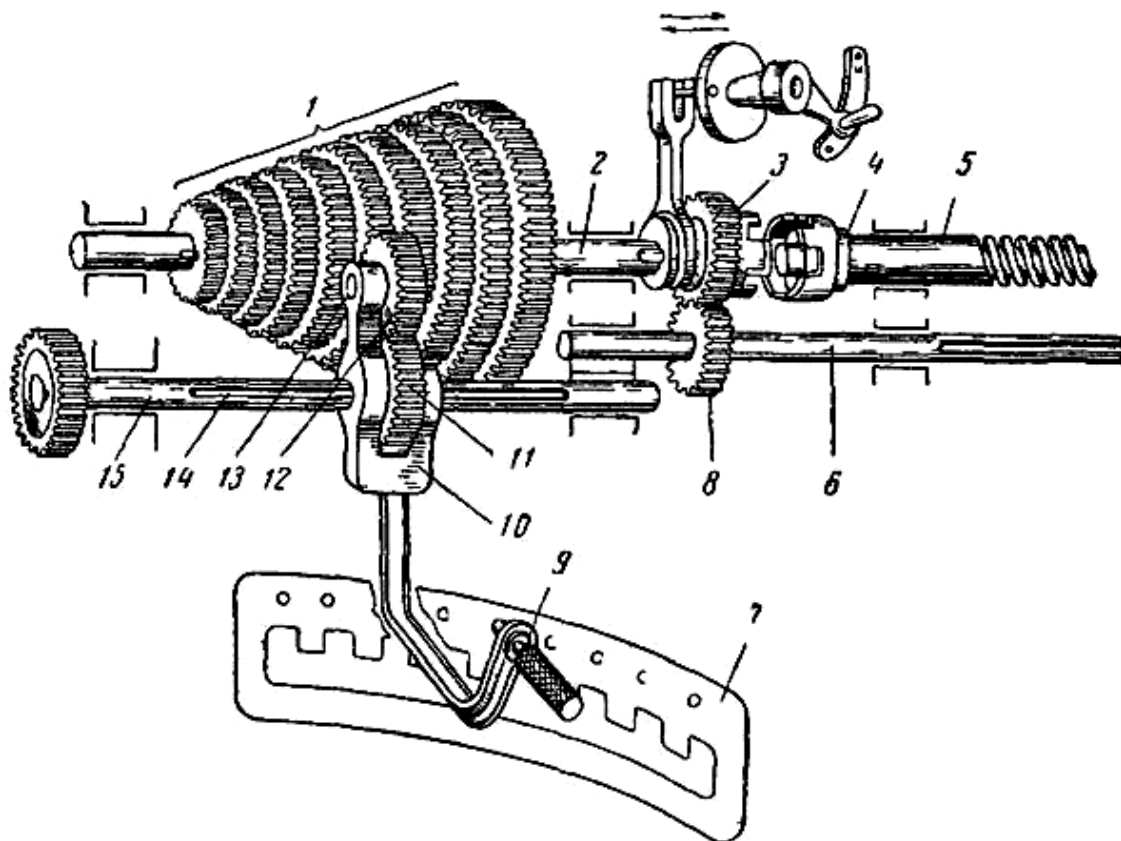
Схема коробки подач с накидным зубчатым колесом
